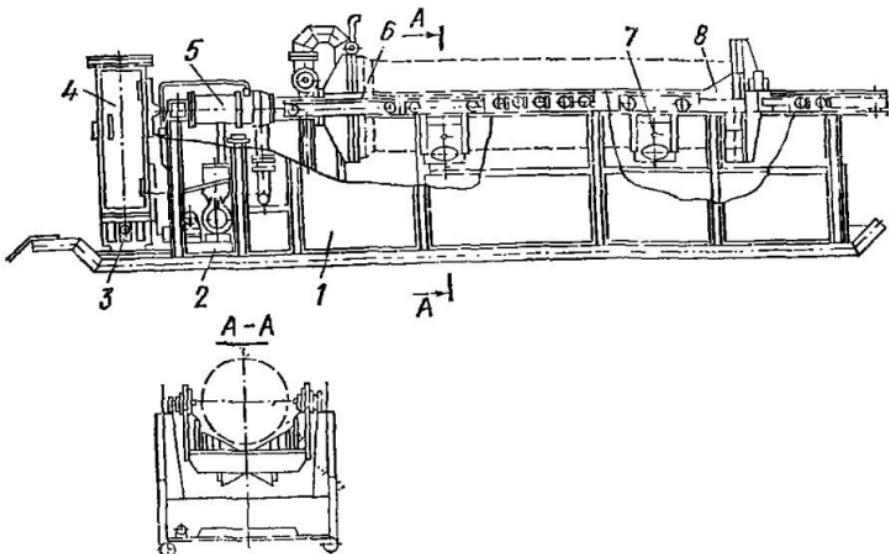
Стенд для опрессовки чугунных и железобетонных труб
